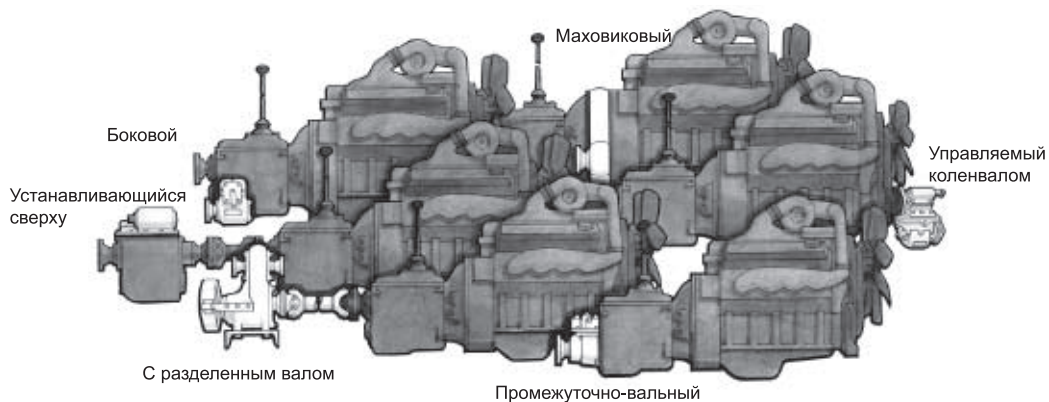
Шесть основных видов MOM: боковой, с разделенным валом, устанавливающийся сверху, промежуточно-вальный, управляемый коленвалом, маховиковый
